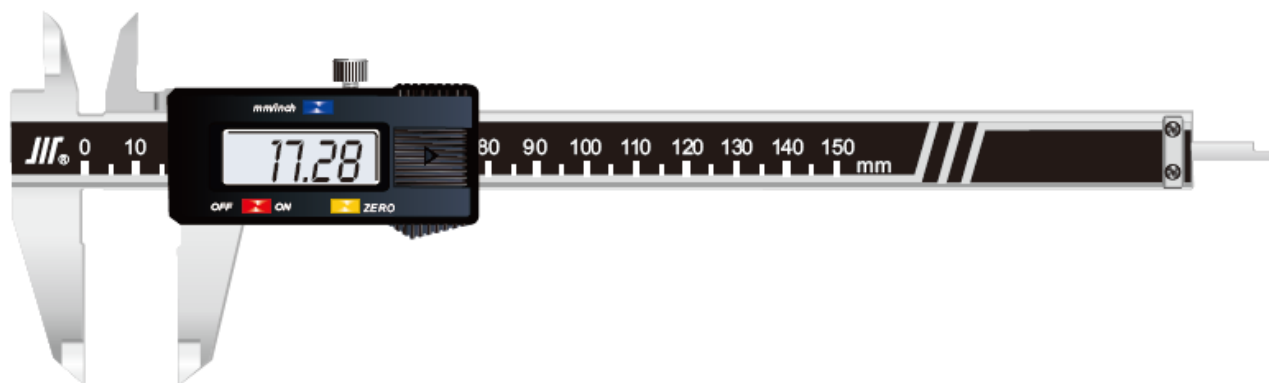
Общий вид штангенциркулей модели ШЦЦ-I
